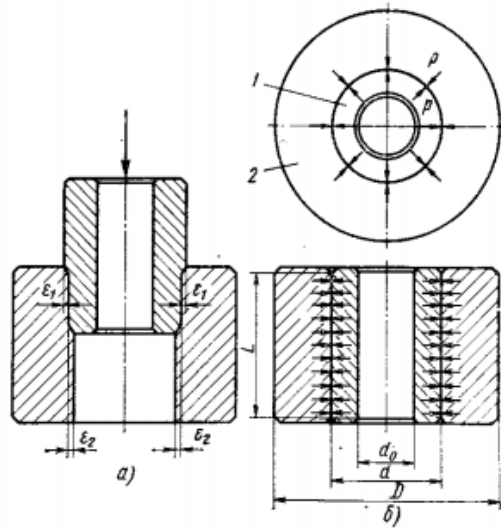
Схема поздовжньо-пресового з'єднання
